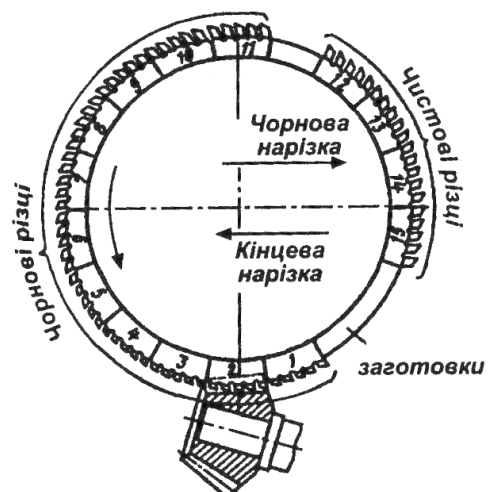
Схема кругового протягування зубів конічного колеса
